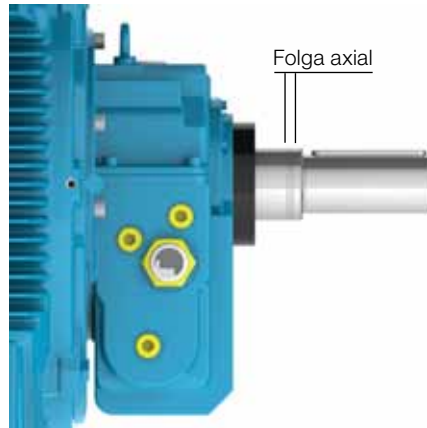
Folga axial em motor equipado com mancal de deslizamento
